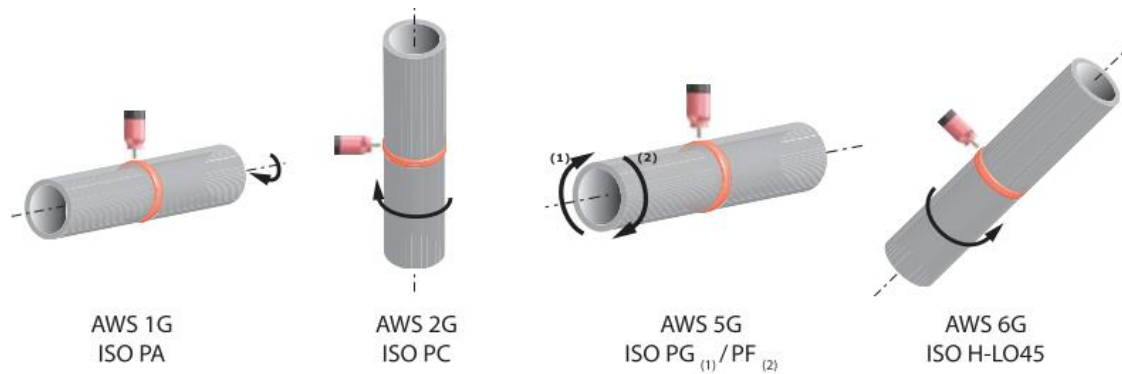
Posições do tubo na soldagem orbital (Fronius, 2010)
